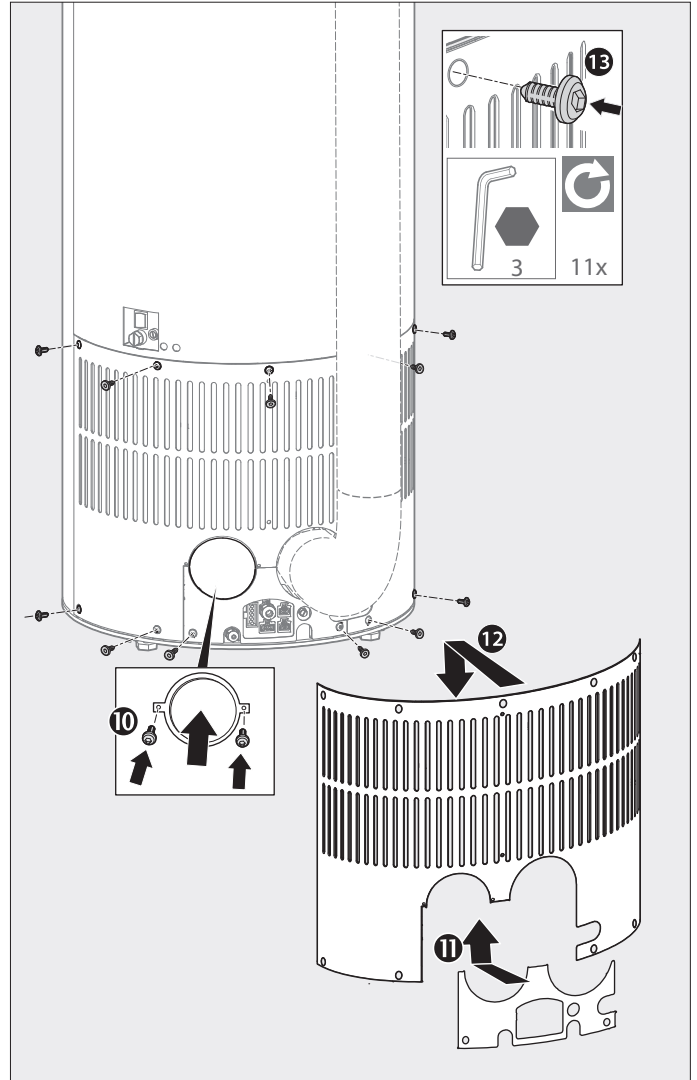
Monter la paroi arrière et le clapet fourni
